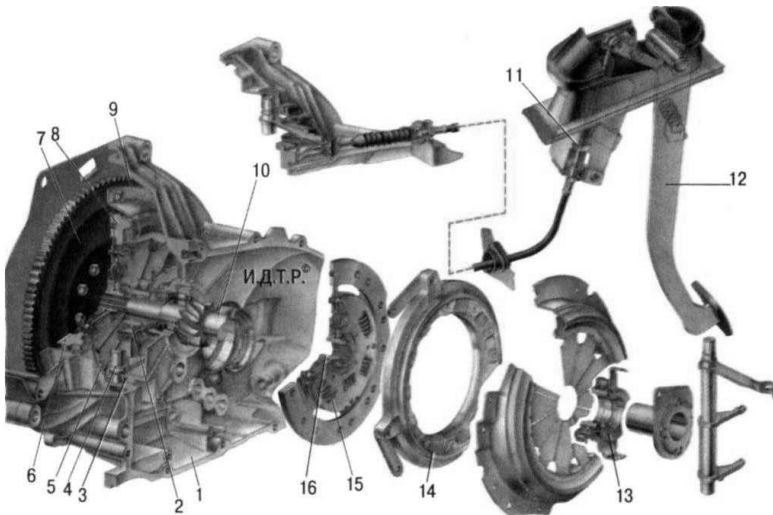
Сцепление: 1 - картер сцепления; 2 - подшипник выключения сцепления; 3 - втулка опорная вала вилки выключения сцепления; 4 - вилка выключения сцепления; 5 - нажимная пружина; 6 - ведомый диск; 7 - маховик; 8 - нажимной диск; 9 - кожух сцепления; 10 - первичный вал коробки передач; 11 - трос; 12 - педаль сцепления; 13 - муфта подшипника выключения сцепления; 14 - пластина, соединяющая кожух сцепления с нажимным диском; 15 - пружина демпфера; 16 - ступица ведомого диска
